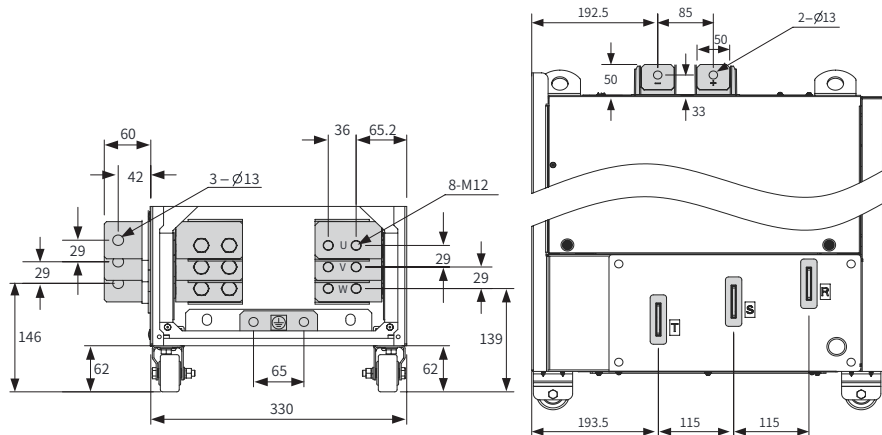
Размеры клемм главной цепи MD880-01S-0538-4/MD880-01S-0605-4 (без выходных реакторов)
